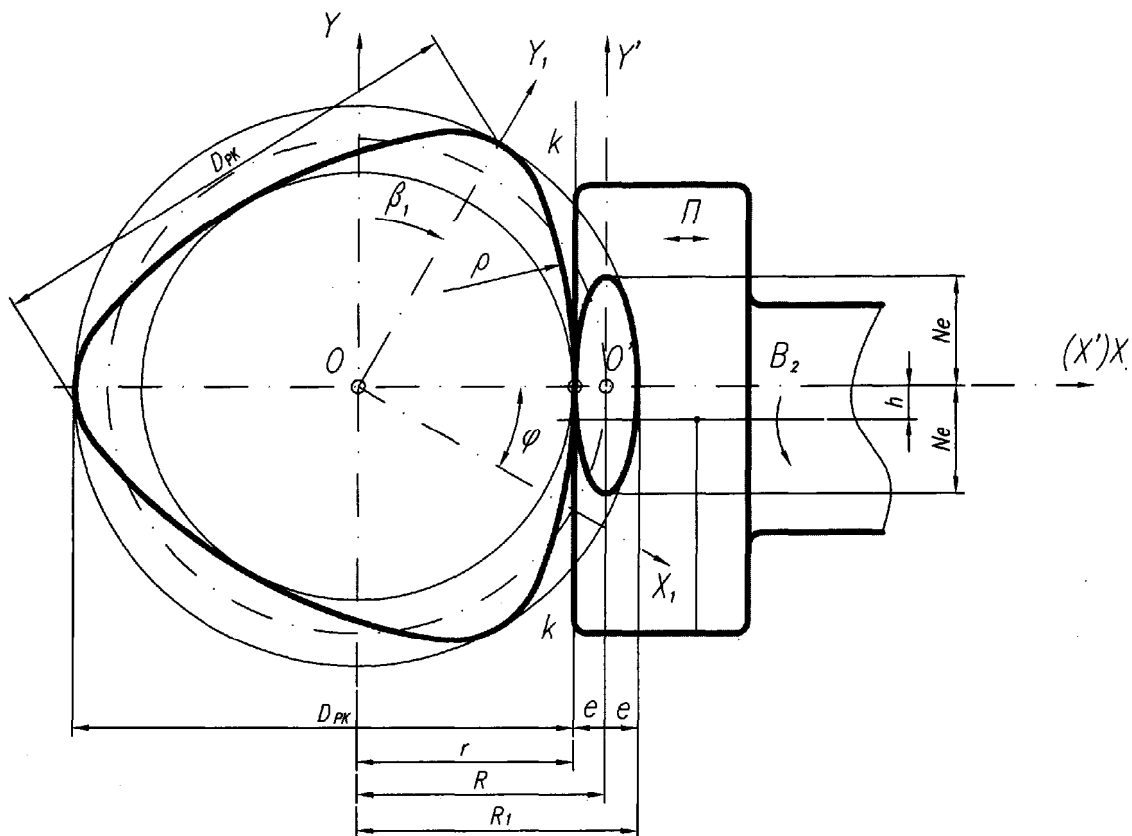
Схема однокоординатной обработки РК-профиля
